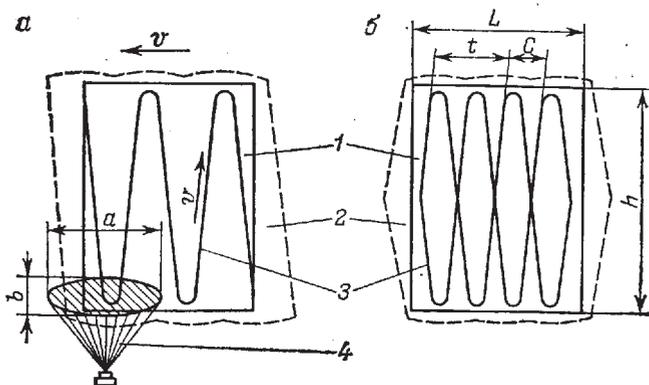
Схема окрашивания с непрерывным возвратно-поступательным движением распылителей и поступательным движением конвейера:
